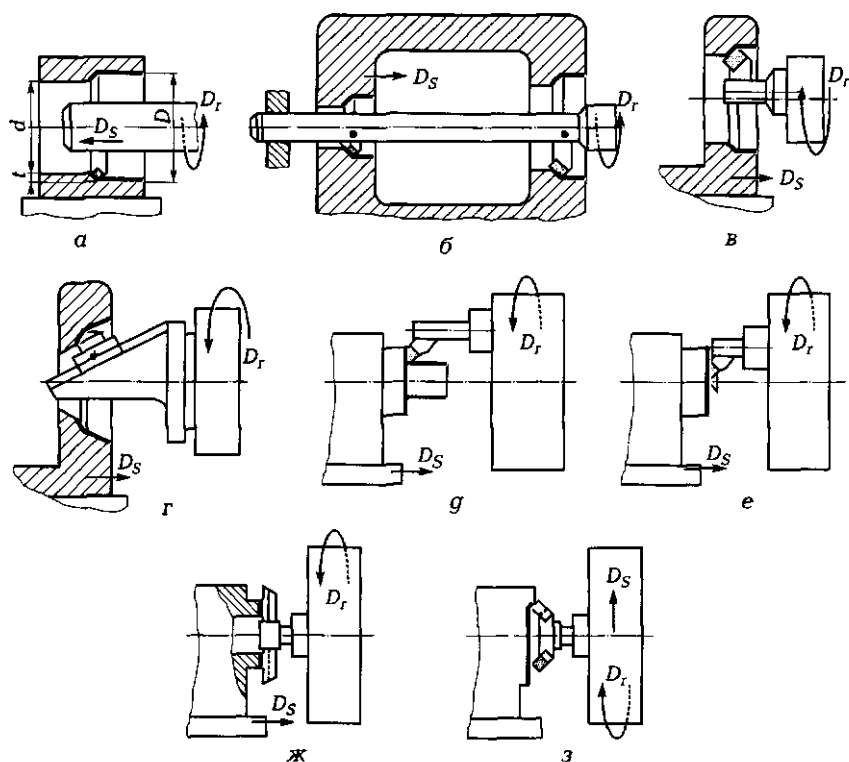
Схемы обработки поверхностей на расточных станках:
